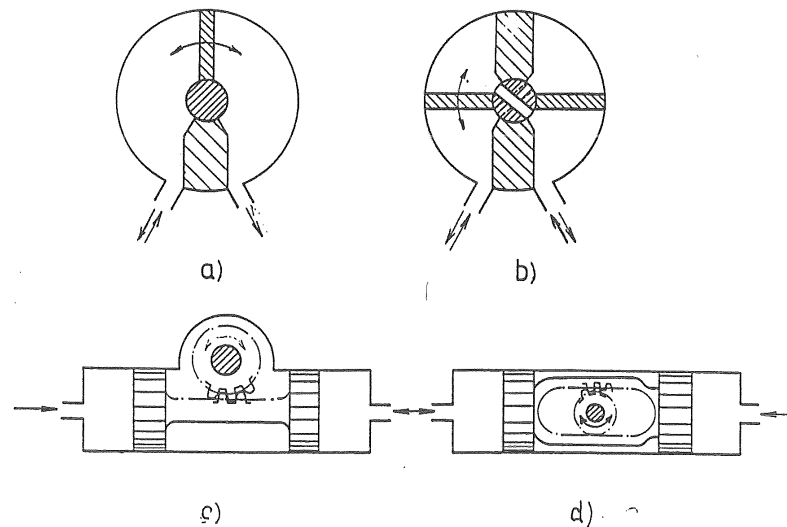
Konstrukční principy přímočarých motorů [12]
